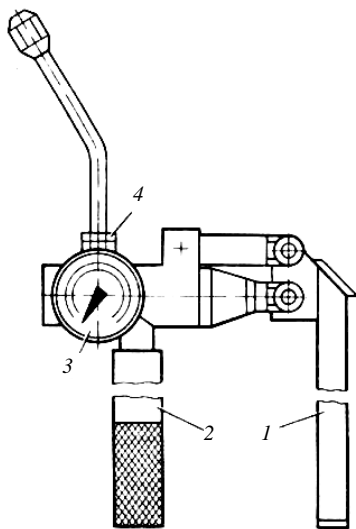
Приспособление КИ-16301А (механотестер) для проверки форсунок:
